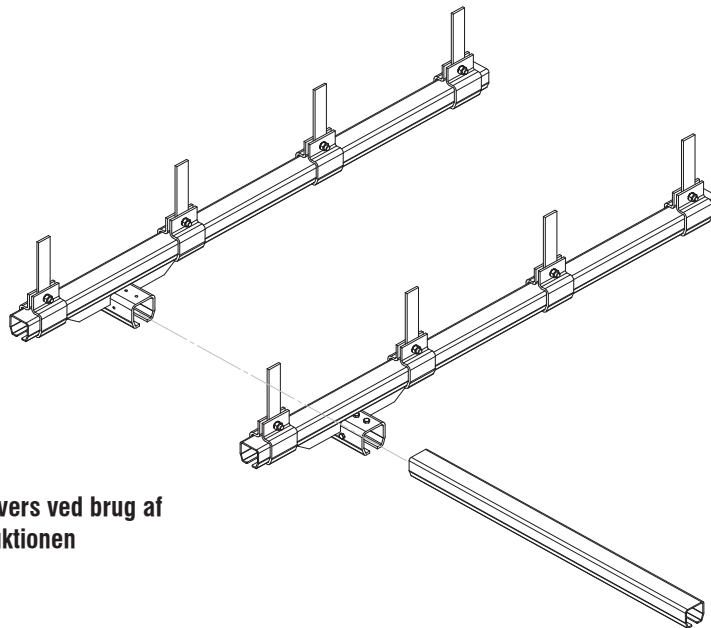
Installation af travers ved brug af den ledige side af konstruktionen
